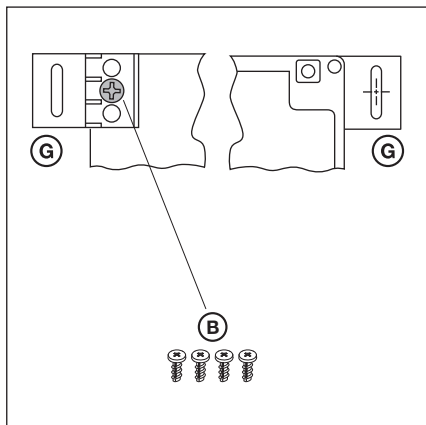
Крепление монтажных опор, вид сзади и спереди
